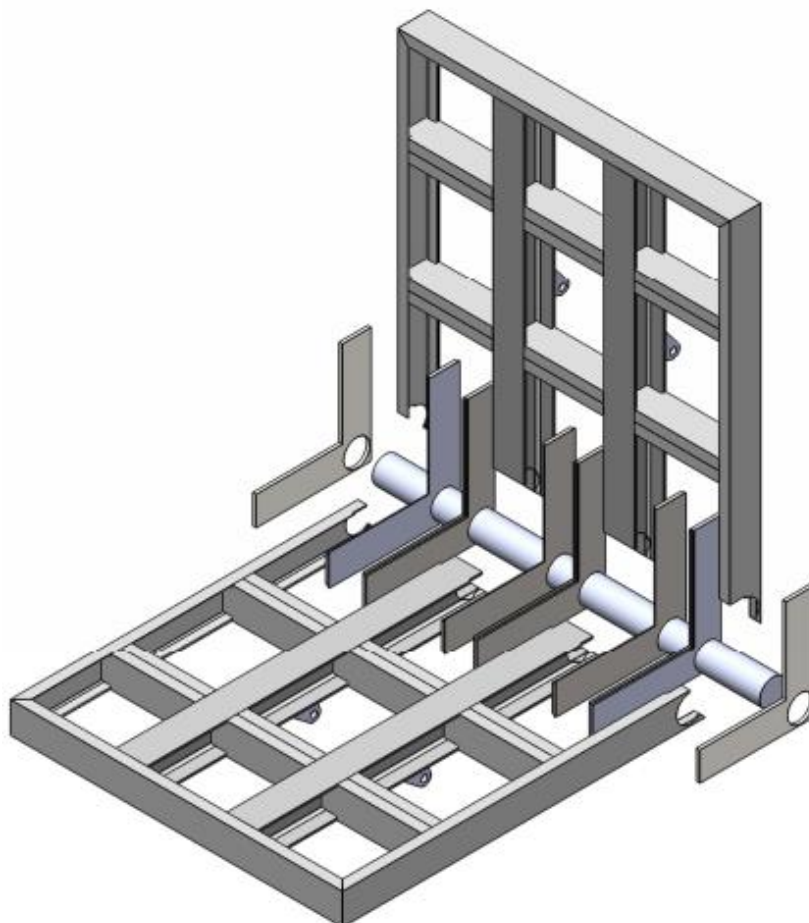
Soldadura parcial do subconjunto Suporte em “L”.
